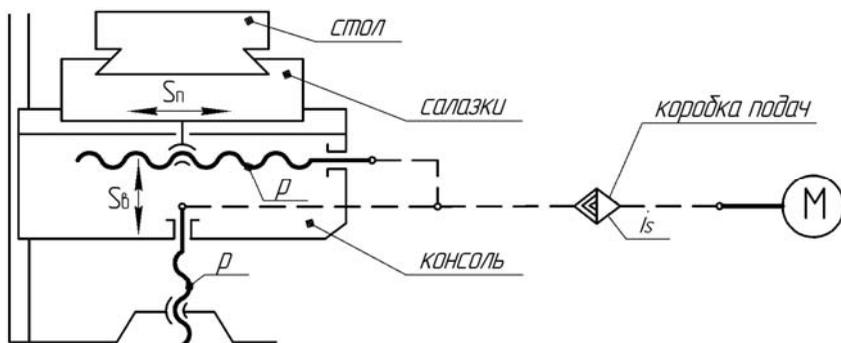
Структурная схема приводов поперечной подачи салазок стола  $s_{п}$  и вертикальной – консоли  $s_{в}$  консольно-фрезерного станка со ступенчатым регулированием с общей коробкой подачи и электродвигателем для всех координатных перемещений
